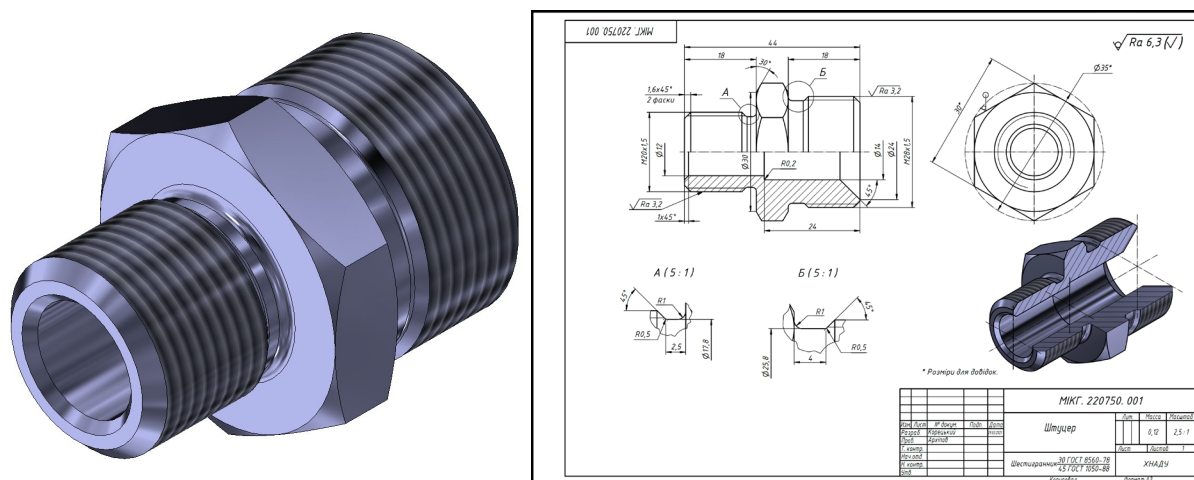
Модель та кресленник деталі типу "Штуцер", що передбачає виготовлення з прутка.
